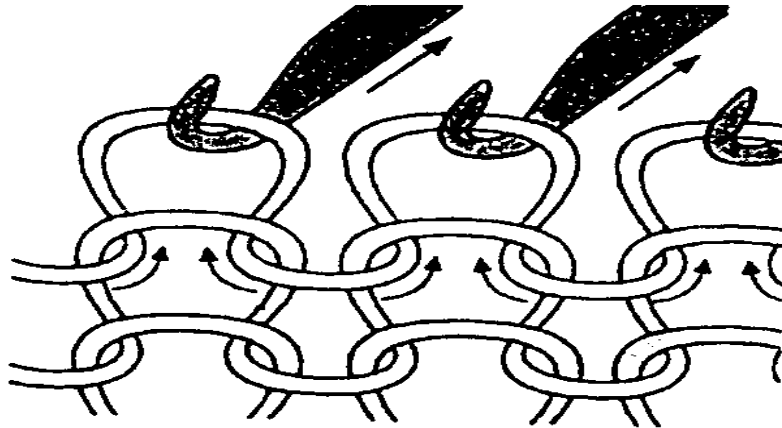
Základní typy tkanin používaných jako výztuže [5]
